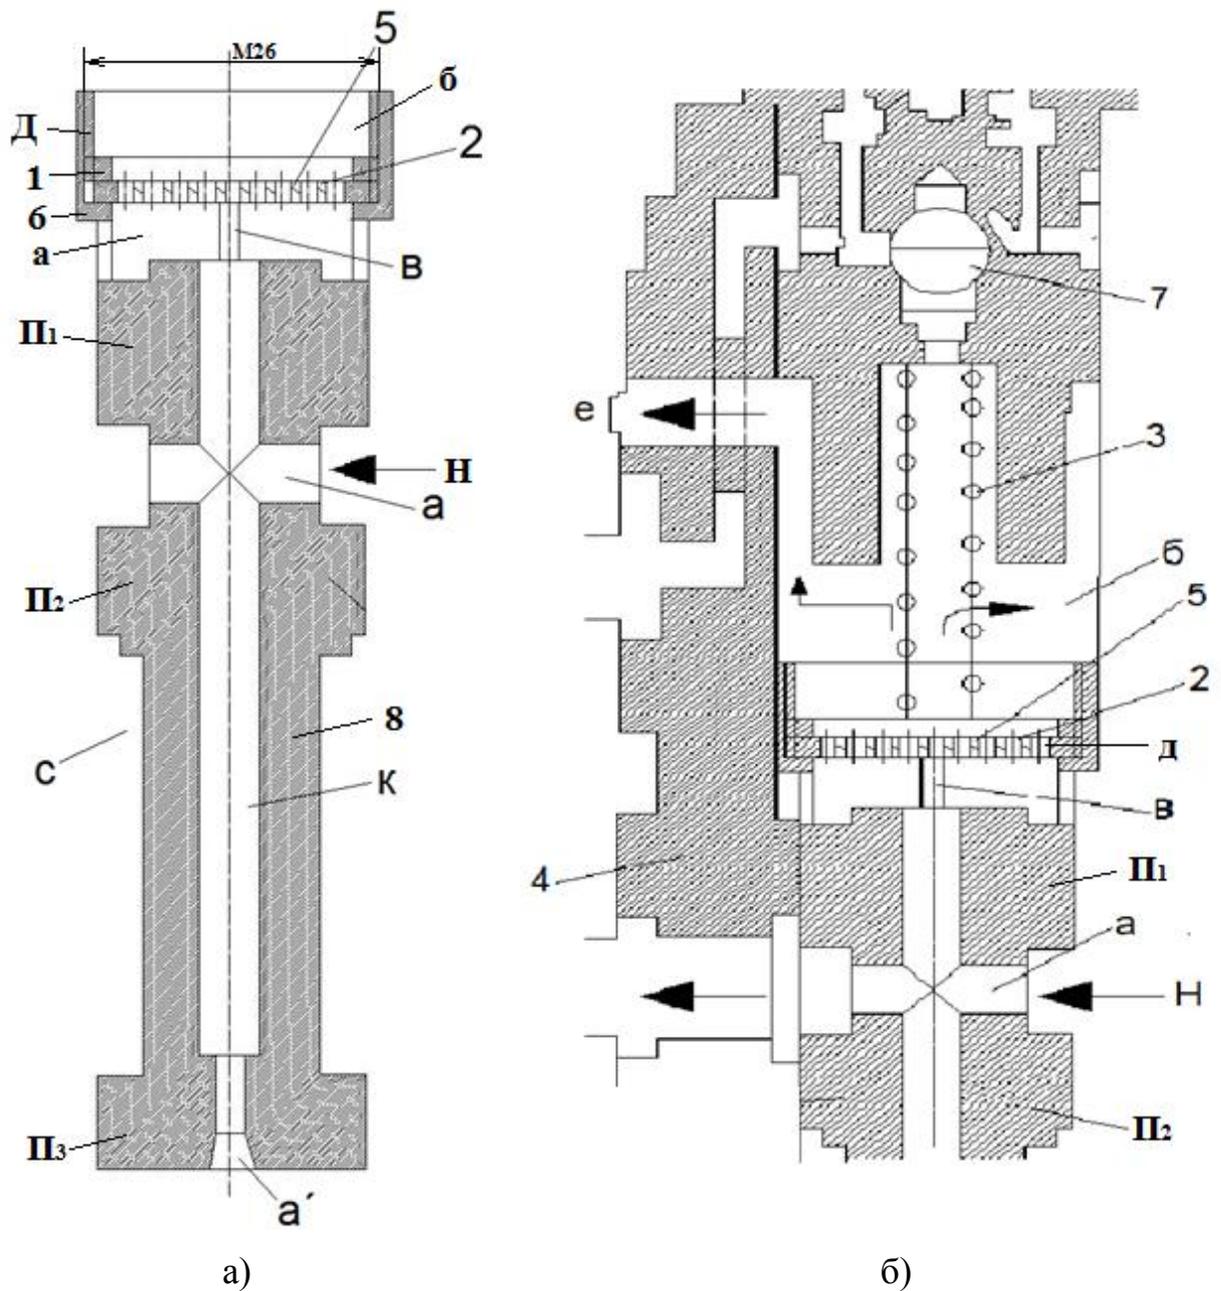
Перепускной клапан: а) с мембраной; б) в сборе 1- гайка; 2- мембрана; 3- пружина; 4- корпус распределителя; 5- отверстие мембраны; 6- демпферный узел; 7- шариковый клапан; Н- нагнетательный трубопровод; а, а', к- направляющие каналы; в, е, С- каналы слива; б- полость.
